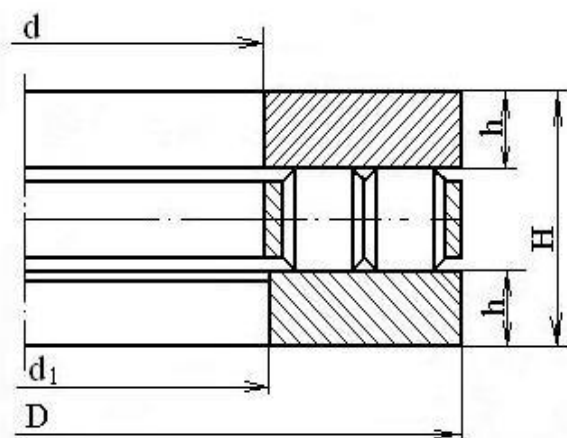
Подшипник роликовый упорный двухрядный
